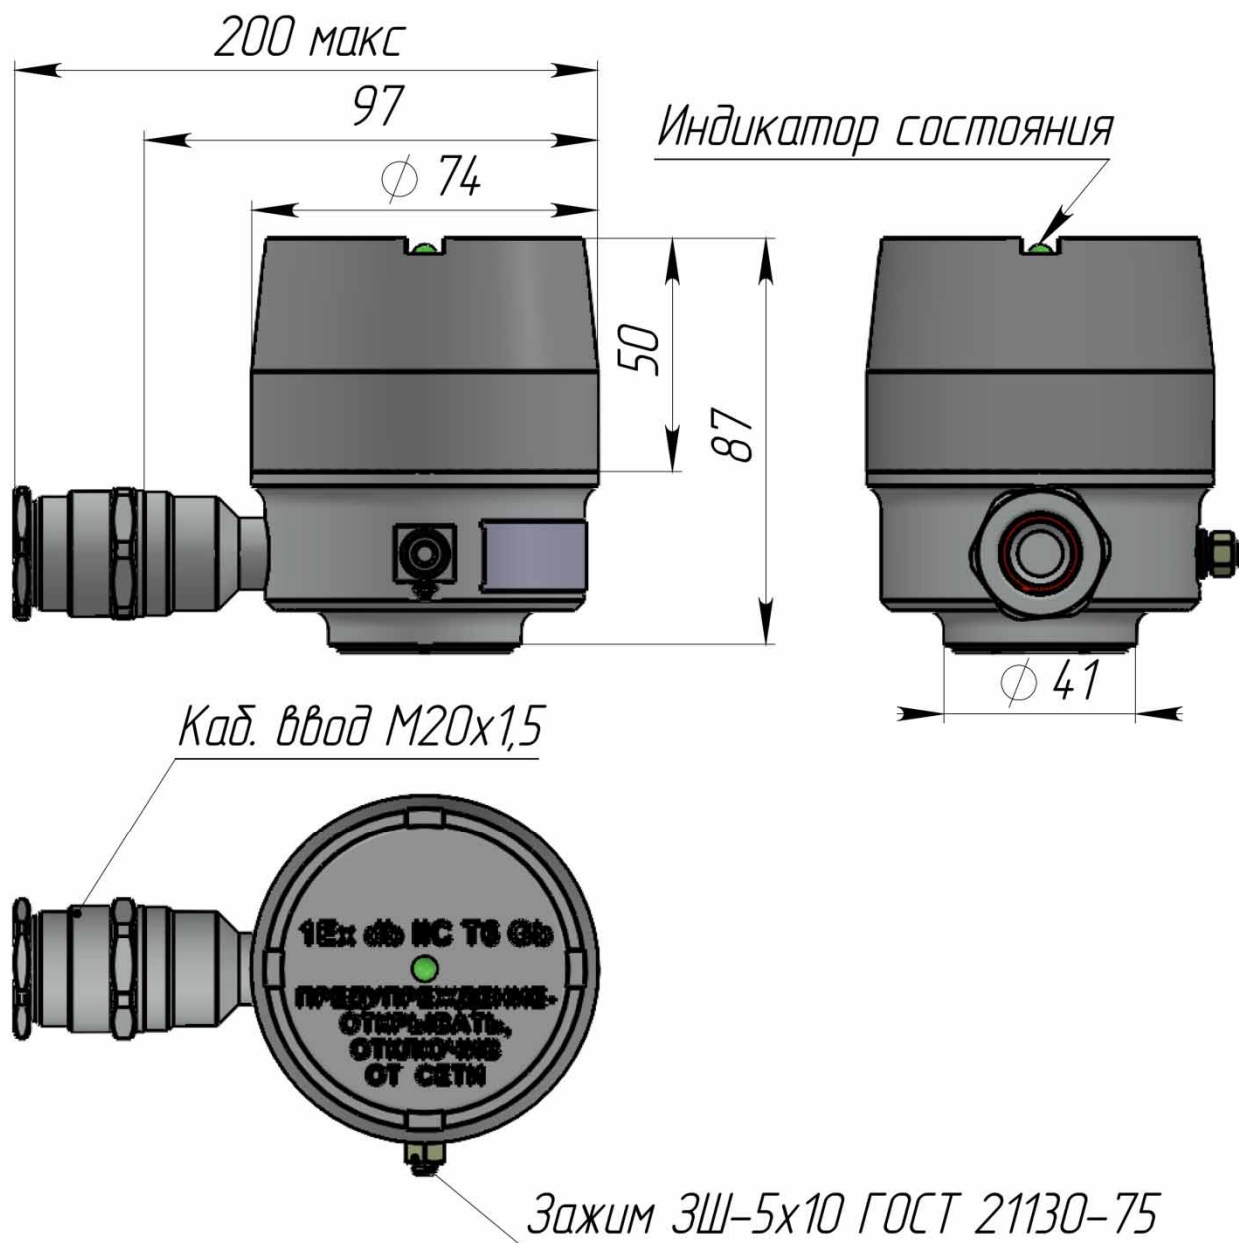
Габаритные размеры корпуса блока электронного в корпусе из нержавеющей стали для оборудования класса безопасности ЗН (высокая крышка)
